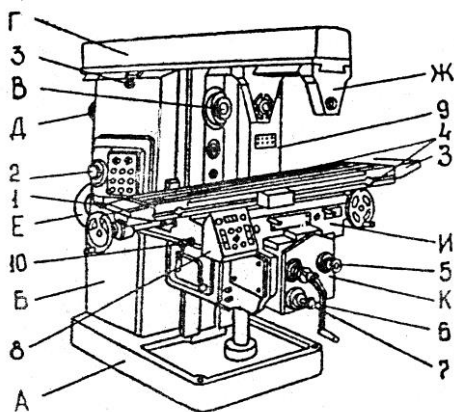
Общий вид горизонтального консольно-фрезерного станка *6Т82Г-1
